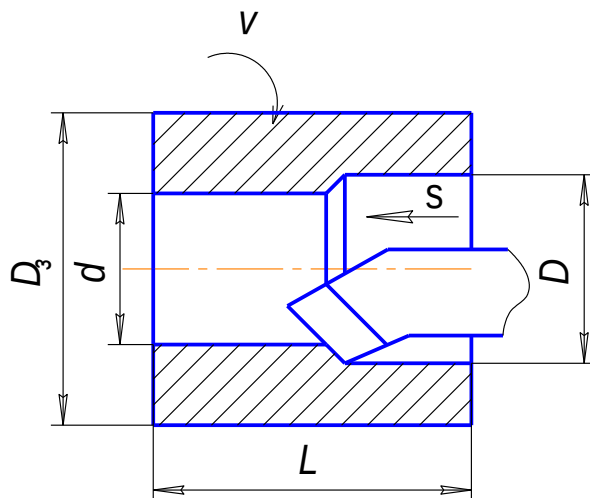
Схема обработки заготовки к задаче 2
